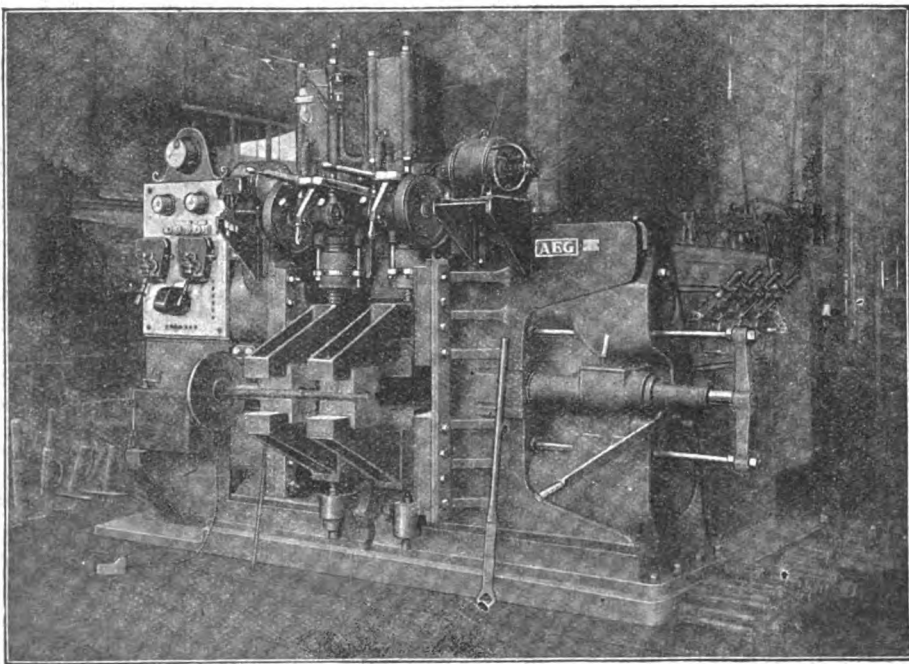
Elektrische Schweißmaschine für Eisenquerschnitte bis zu 6000 qmm in der Eisenbahnhauptwerkstatt Ponarth.
